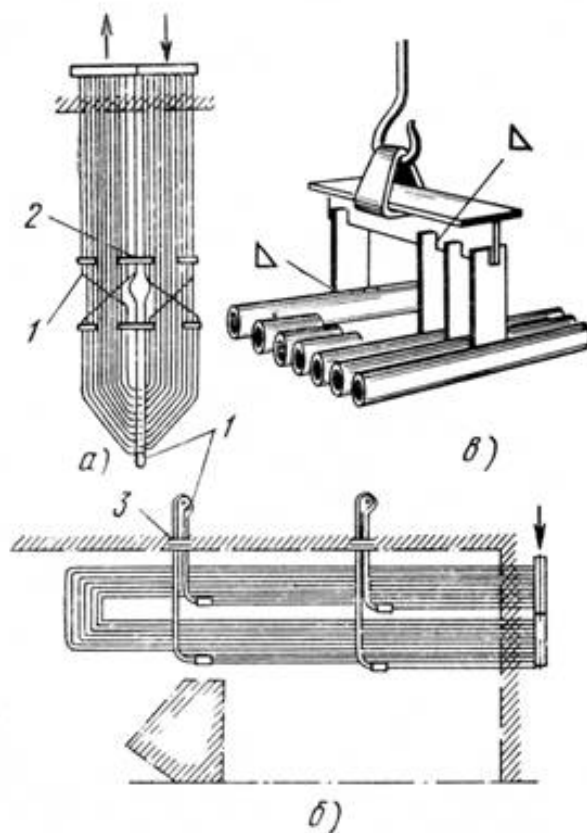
Крепление вертикальной (а), горизонтальной (б) и потолочных труб (в) пароперегревателя (треугольником указаны места сварки):
